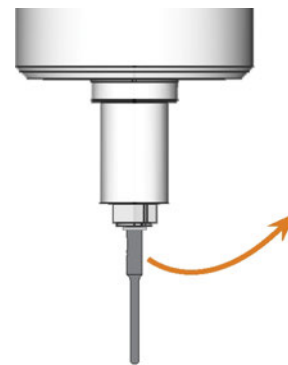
Das Werkzeug aus der Spannzange entfernen
